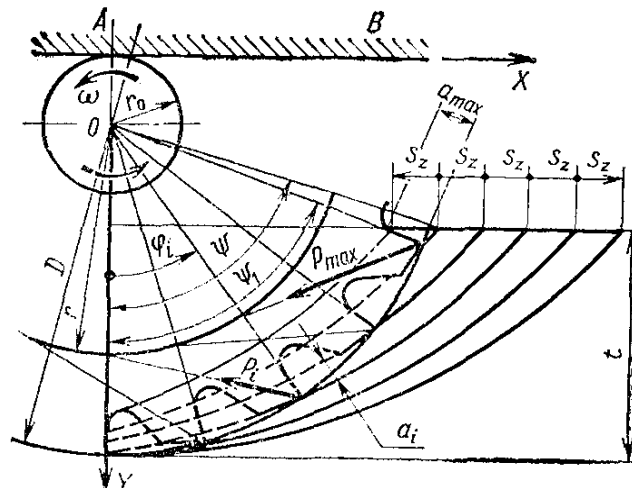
Розрахункова схема зустрічного циліндричного фрезерування
